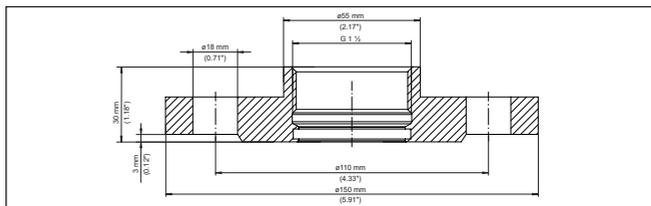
Dimensions adaptateur de filetage G $\frac{1}{2}$ (DIN 3852-X) sur bride DN 40 (EN 1092-1, forme B1) PN 40
